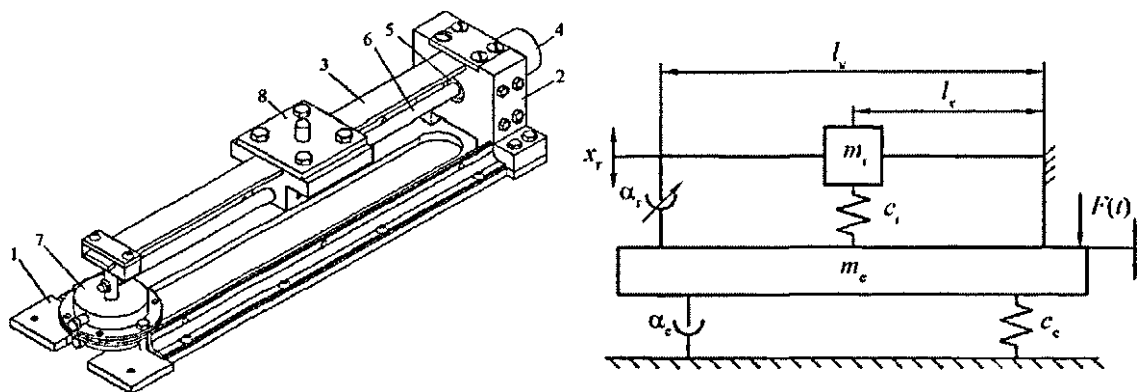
Динамічний віброгасник коливань: 1) основа; 2) корпус; 3) пружний елемент; 4) кроковий двигун; 5) кульова опора; 6) ходовий гвинт; 7) пневматичний демпфер; 8) рухома маса з вбудованою гайкою кочення
